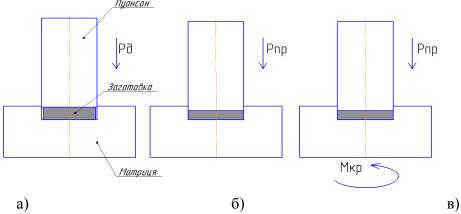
Схема процесса перед осадкой (а) после осадки (б); кручение под давлением (в): Рд - усилие деформирования при осадке; Рпр - усилие прижима пуансоном заготовки; Мкр - момент необходим для кручения заготовки.
